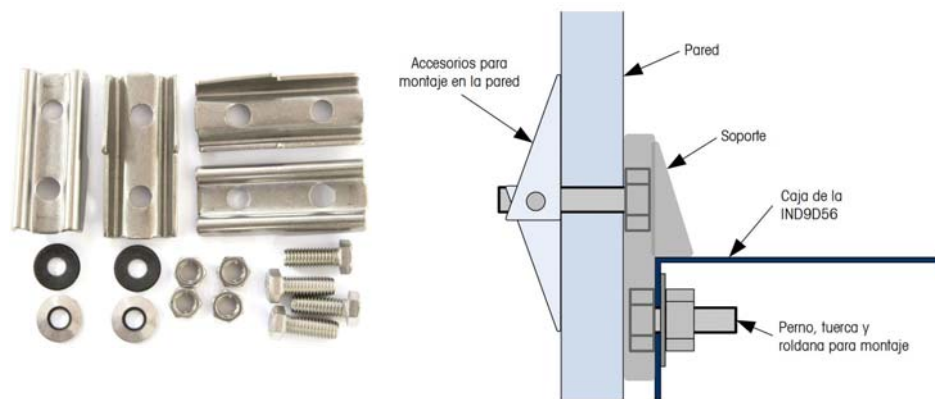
Juego de soportes para montaje en pared (izquierda) y método de montaje (derecha)
